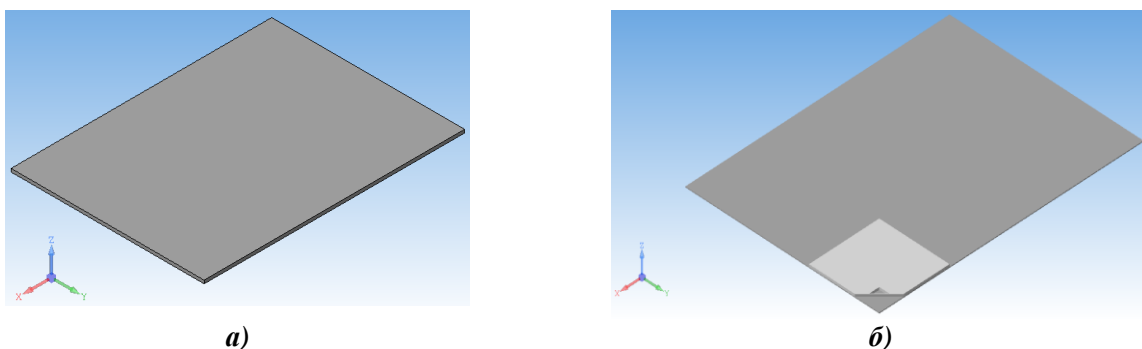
Система шаблон-заготовка: а – заготовка; б – одна із можливих комбінацій
